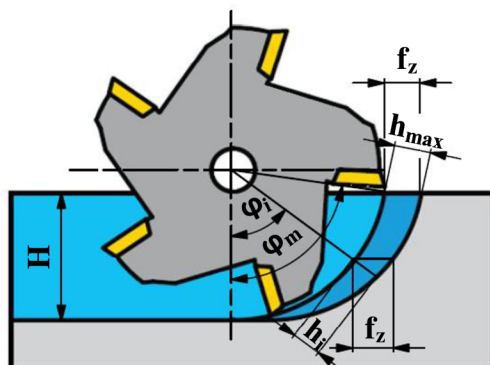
Vliv polohy osy frézy vůči obrobku na utváření třísky při nesousledném frézování [8].
